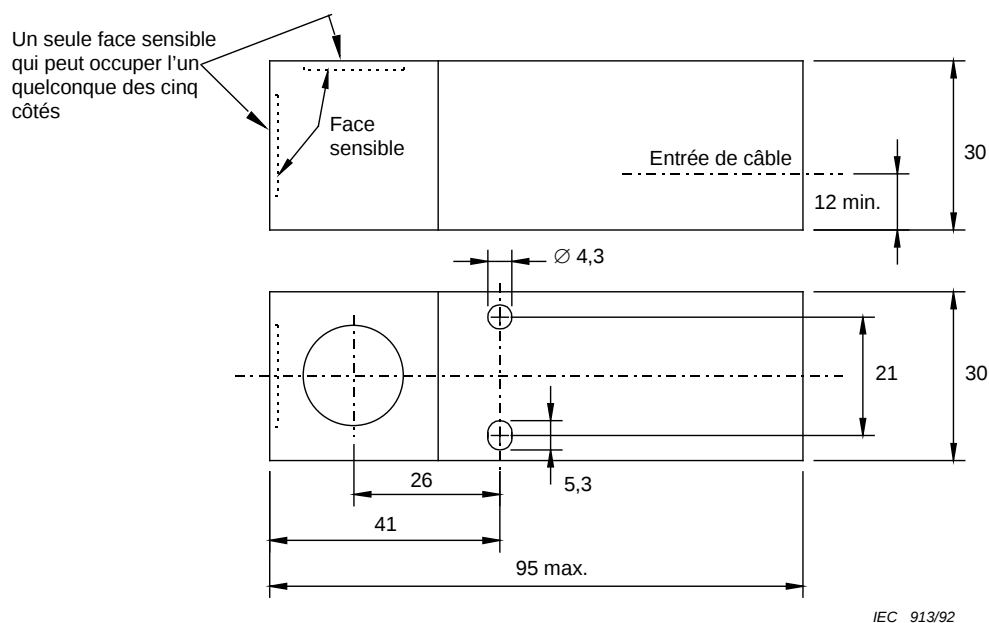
(CC) a – Dimensions, type C30 en millimètres
